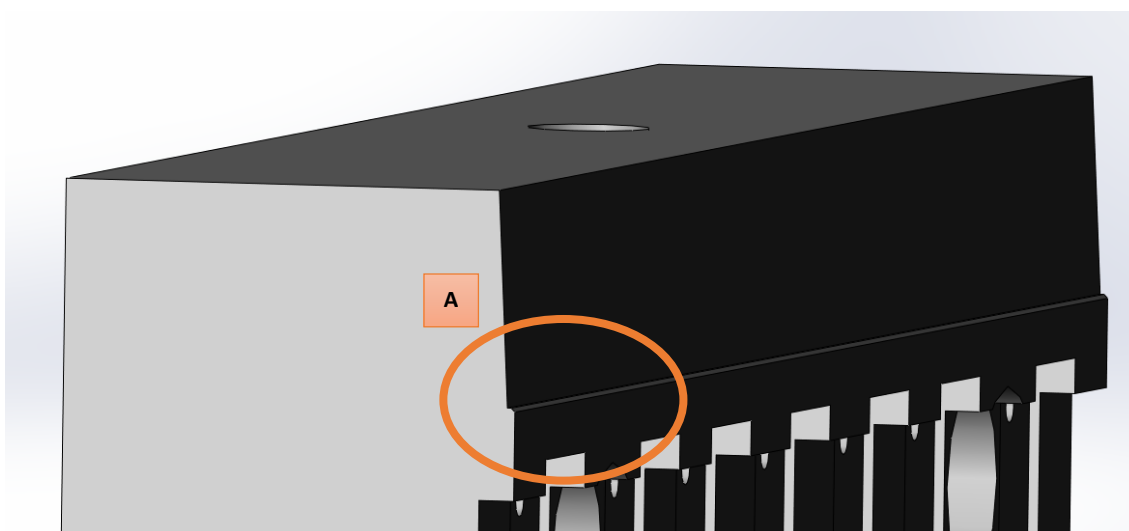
Zona de difícil maquinagem - Suporte_5 - Mola de lâmina
